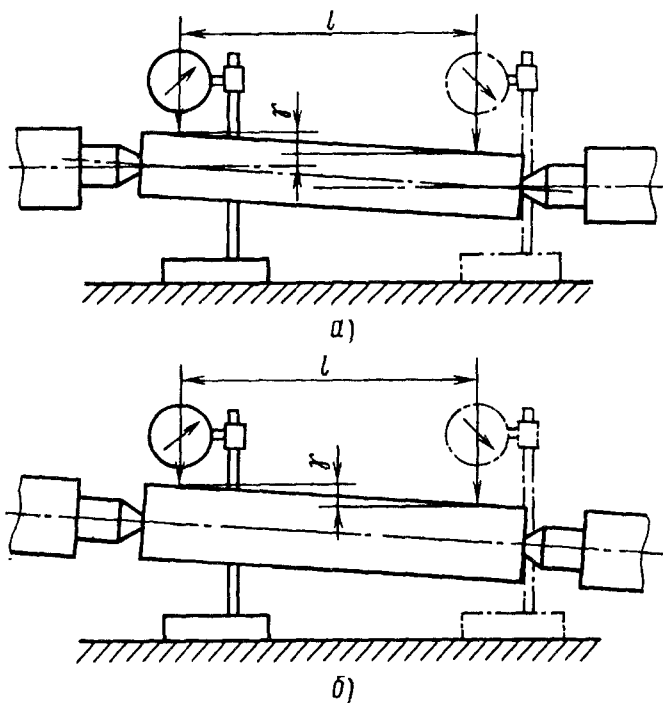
Контроль соосности центров токарного станка с помощью оправки
